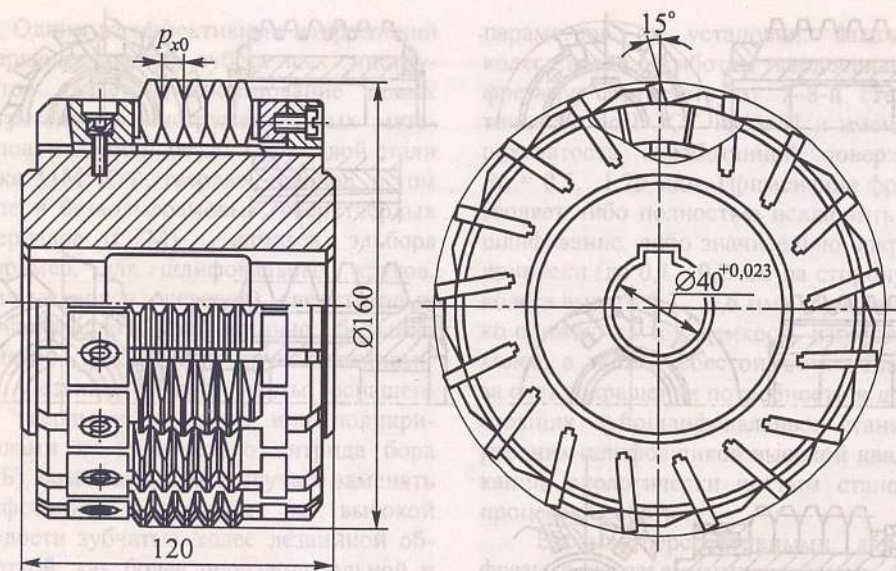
Сборная червячная фреза с многогранными твердосплавными пластинами
